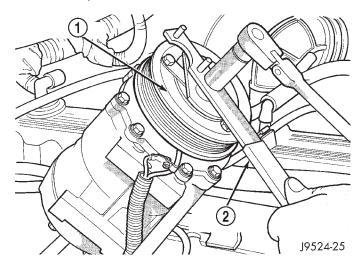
DESMONTAJE DE TUERCA DEL EMBRAGUE
